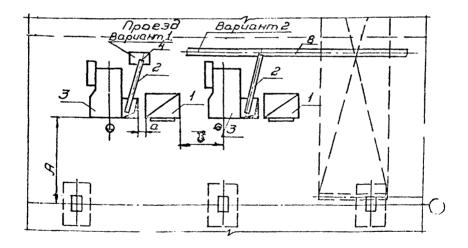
Схема расположения штамповочных линий на базе ГКМ: I — нагревательная печь; 2 — транспортер; 3 — горизонтально-ковочная машина; 4 — тара.
